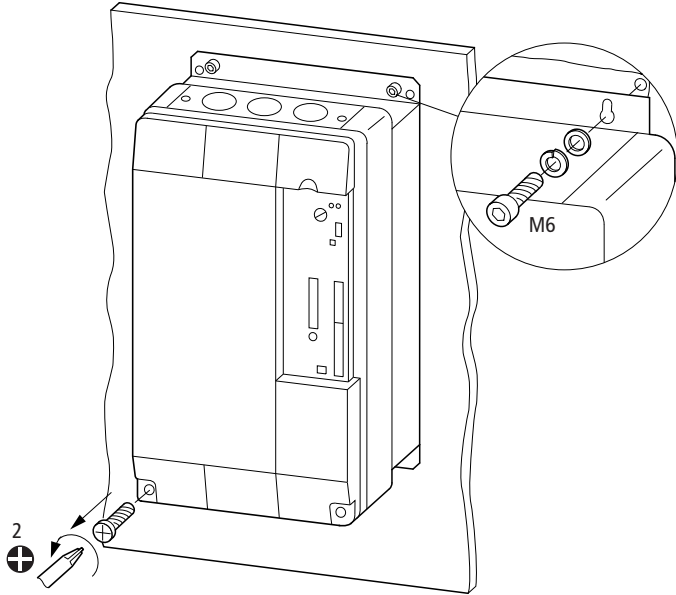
Befestigung auf Montageplatte DM4-340-7K5 bis DM4-340-200K
